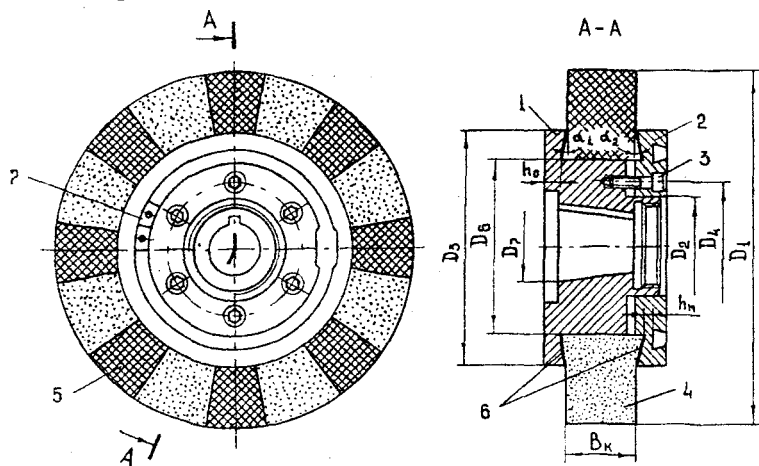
Сборный композиционный круг: 1 - основной фланец; 2 - прижимной фланец; 3 - винт; 4 - абразивный сегмент; 5 - смазывающе-охлаждающий сегмент; 6 - картонная прокладка; 7 - балансированный сухарик
